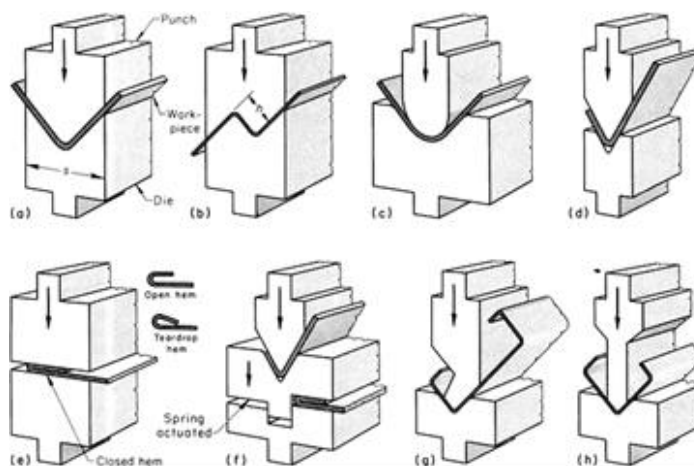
Processos de quinagem, incluindo quinagem composta (wikiEngenharia, consult. 2013).
